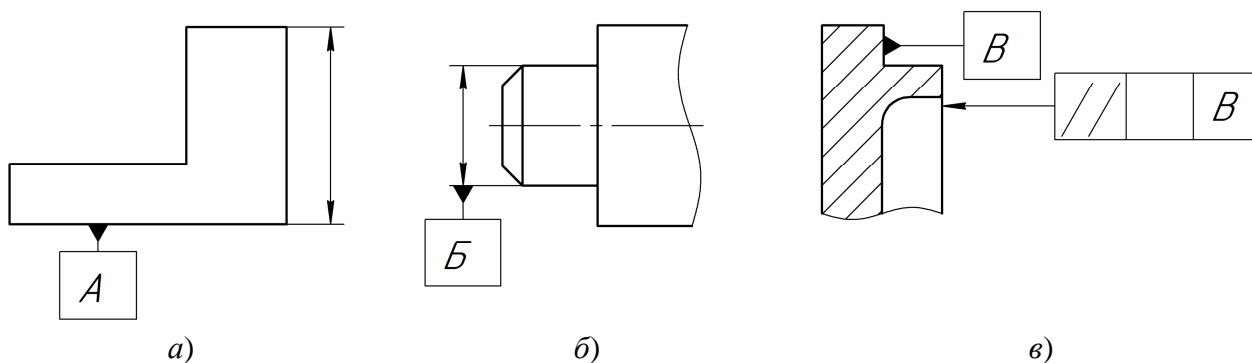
Примеры нанесения на чертежи деталей условных обозначений баз
